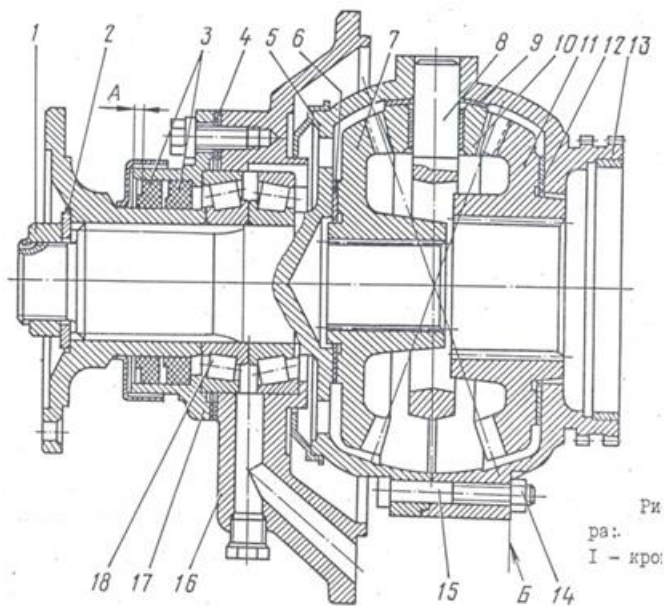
Диференціал міжосьовий: 1 – гайка; 2 – пружина тарілчаста; 3 – манжета; 4 – прокладка; 5 – чашка диференціала; 6 – шайба опорна; 7 – шестерня; 8 – хрестовина; 9 – шайба опорна; 10 – сателіт; 11 – шестерня; 12 – шайба опорна; 13 – чашка диференціала; 14 – гайка; 15 – болт; 16 – гніздо підшипників; 17 – кришка; 18 – підшипник роликовий; А – розмір; Б – поверхня.
